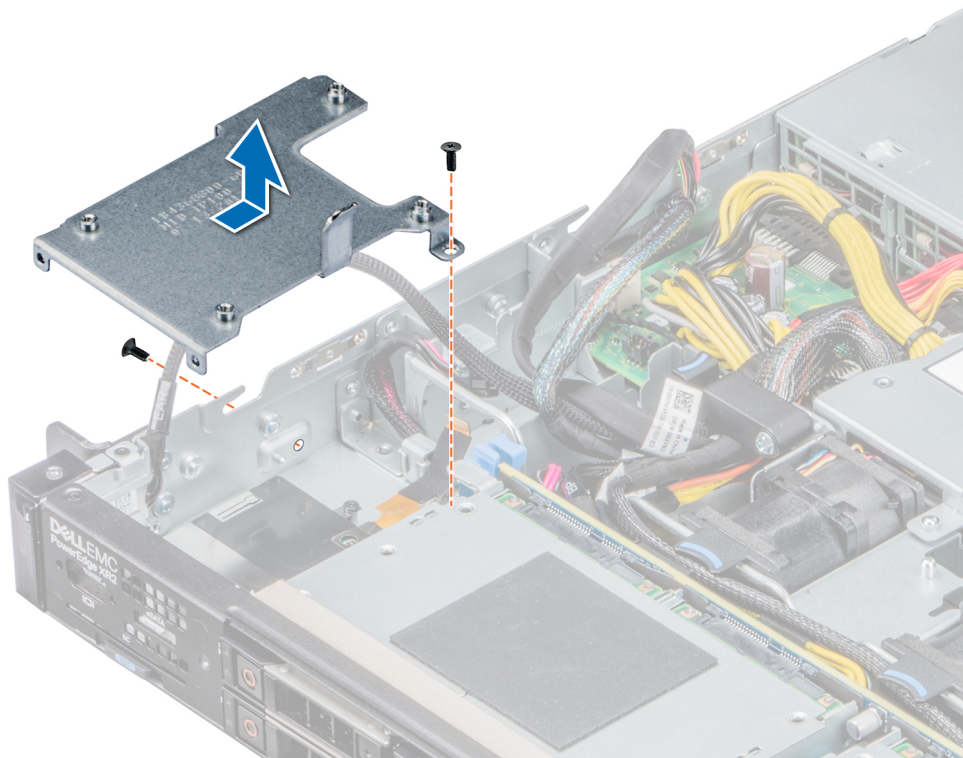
Entfernen der Smart-Card-Leser-Halterung
